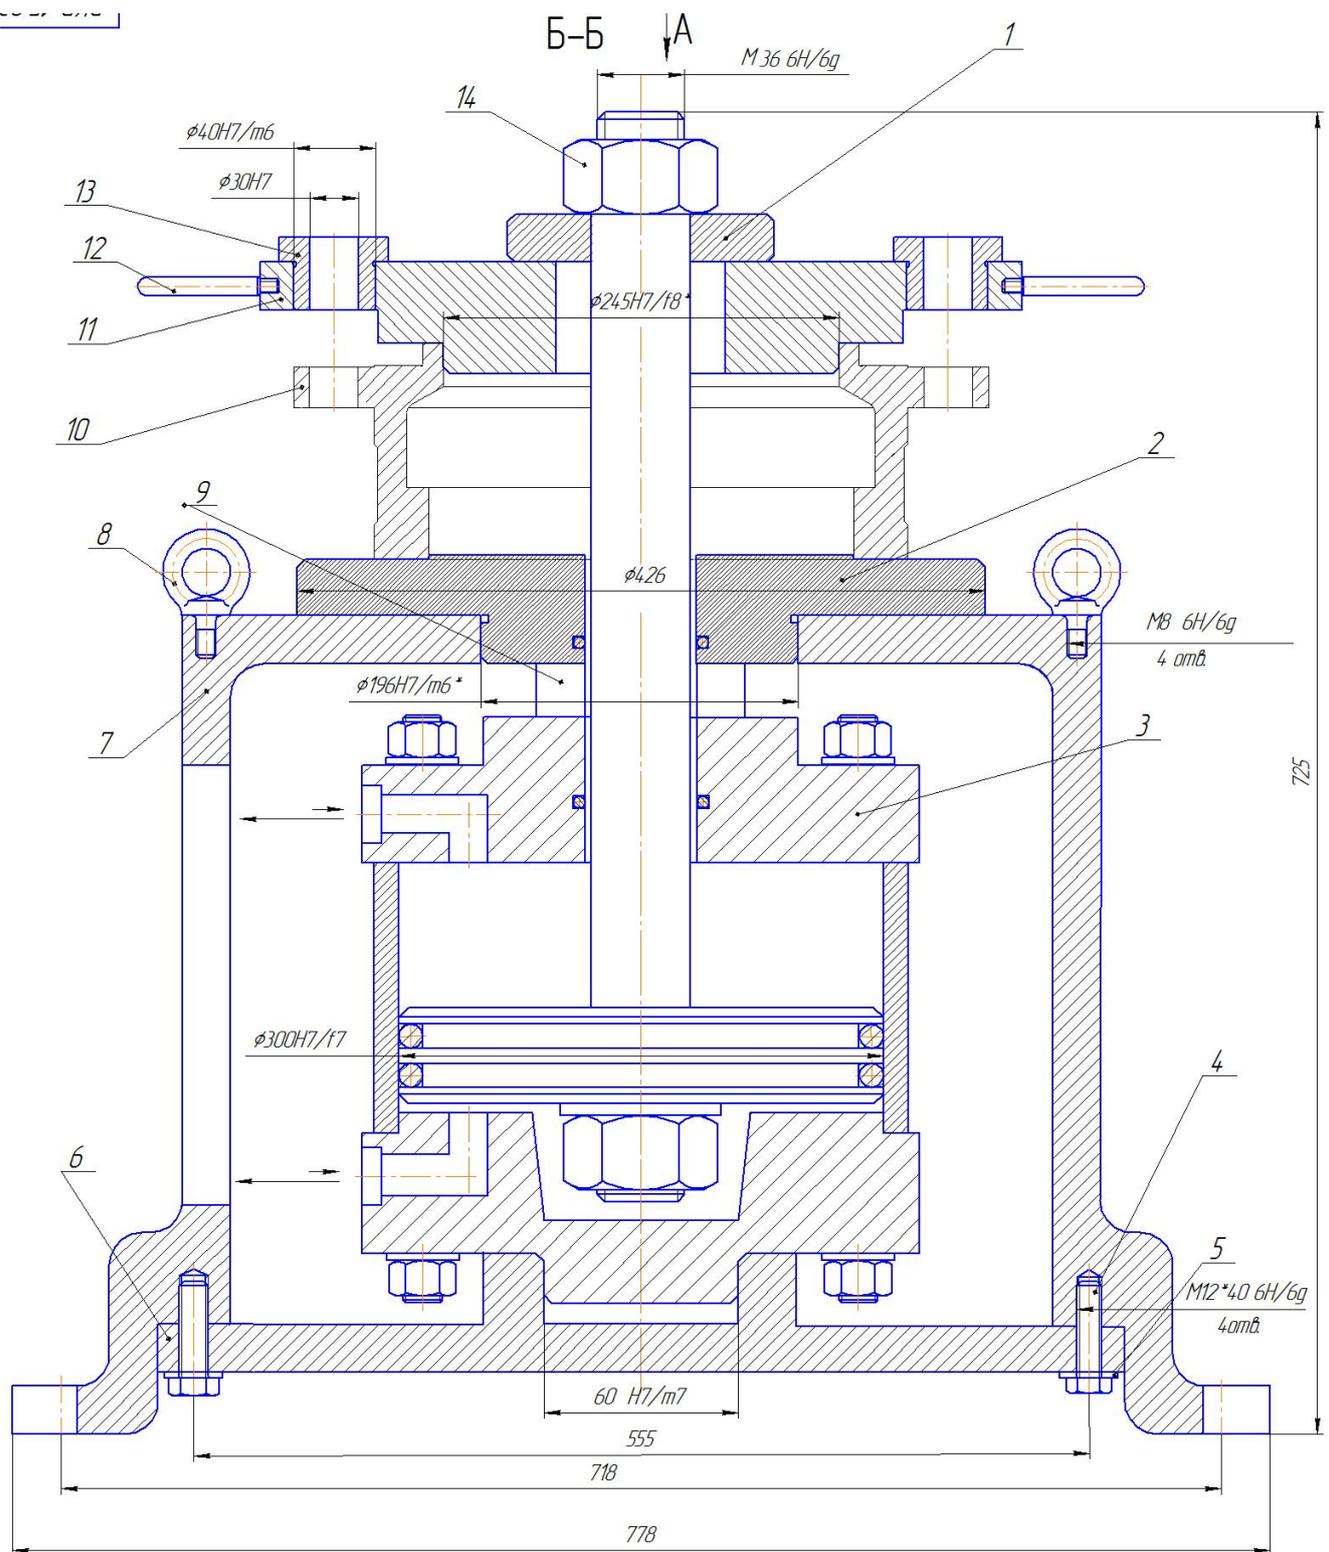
Общий вид приспособления для сверления отверстий
